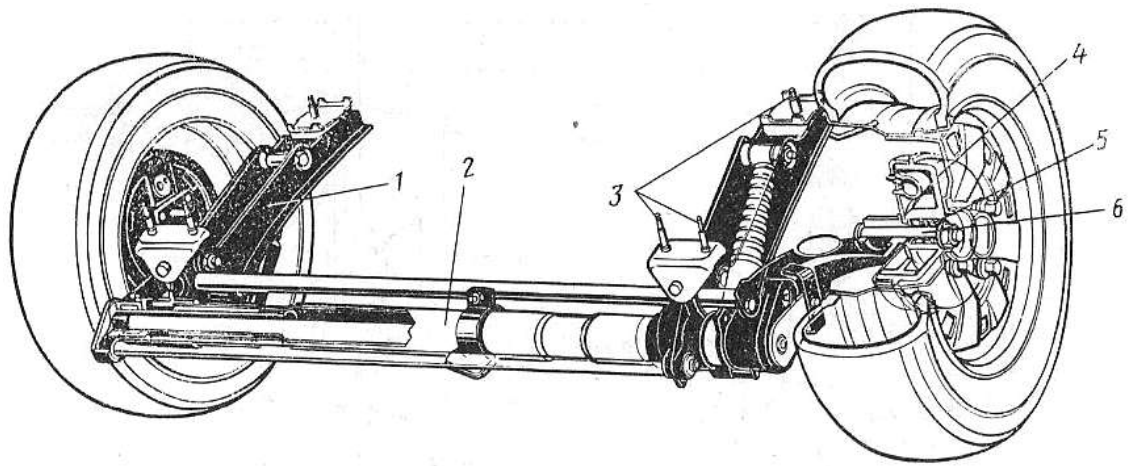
Задня підвіска автомобіля «Пежо 205»: 1 - кронштейни; 2 - поперечна труба; 3 - різьбові елементи; 4 - гальмівний барабан; 5 - підшипник; 6 - цапфа
